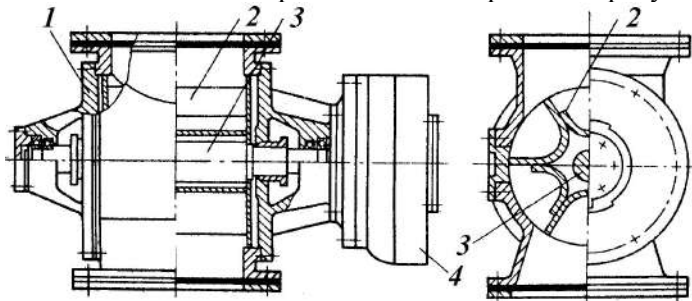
Шлюзовой питатель: 1 – корпус; 2 – ротор; 3 – вал; 4 – редуктор.
